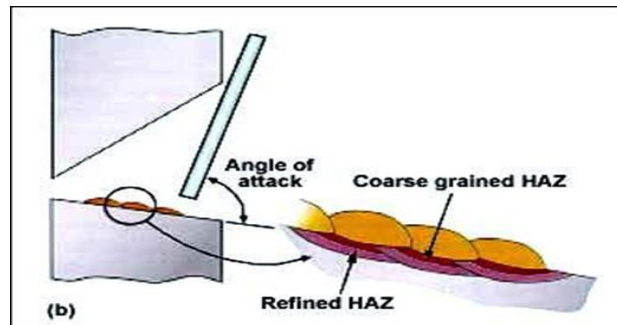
Soudage en position verticale ou horizontale – faible degré de raffinement de la ZAT. [12]
